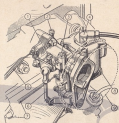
Carburatore Solex (serie d'aspiratore sulla presa d'aria).
